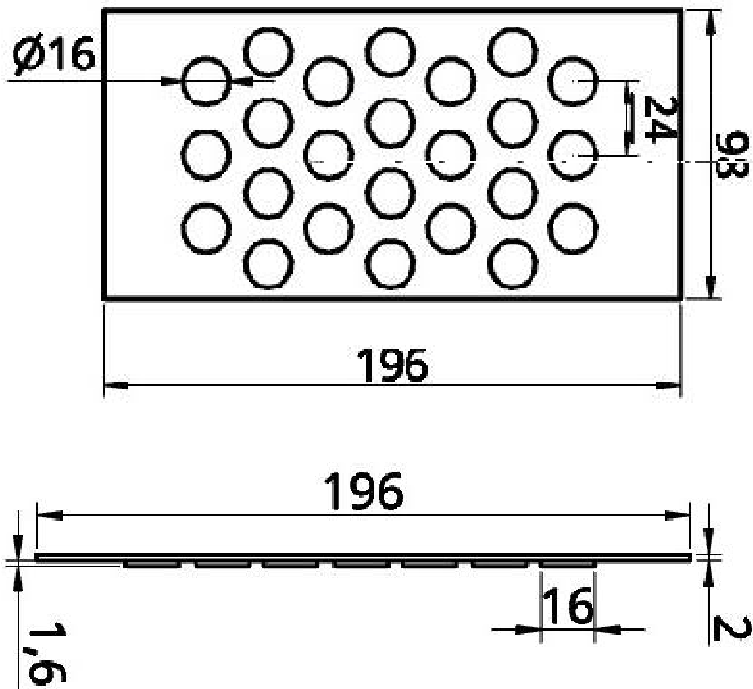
Схема поверхности щелевого канала с цилиндрическими лунками
